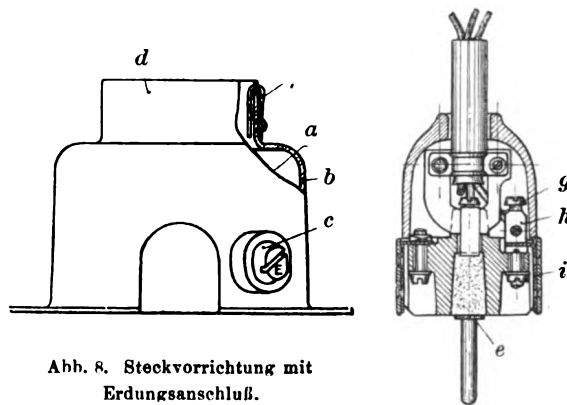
Steckvorrichtung mit Erdungsanschluß.
